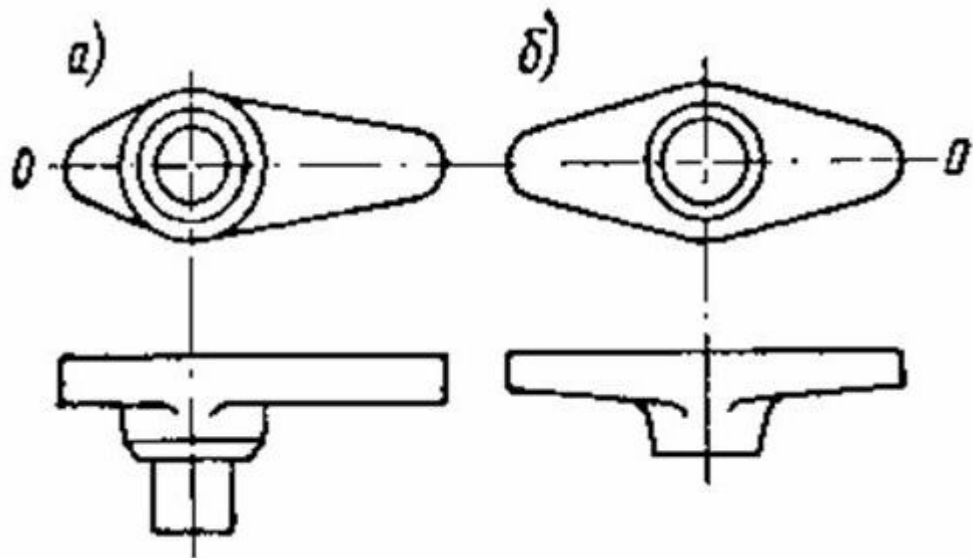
Приклади деталей закріплених в двокулачковому патроні
